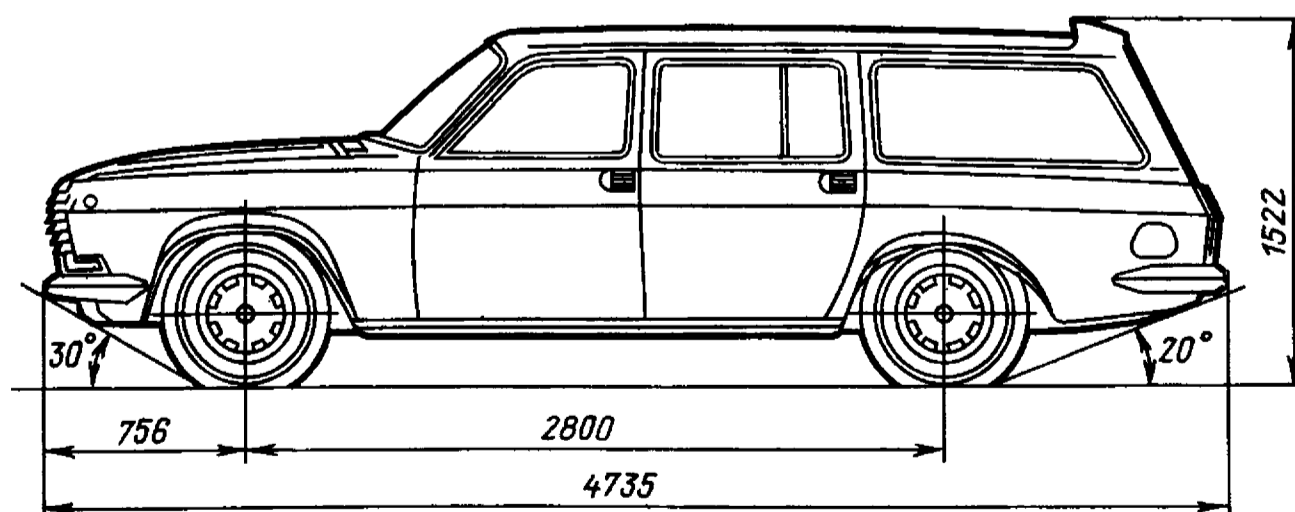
Автомобиль ГАЗ-24-12 «Волга» и его габаритные размеры
